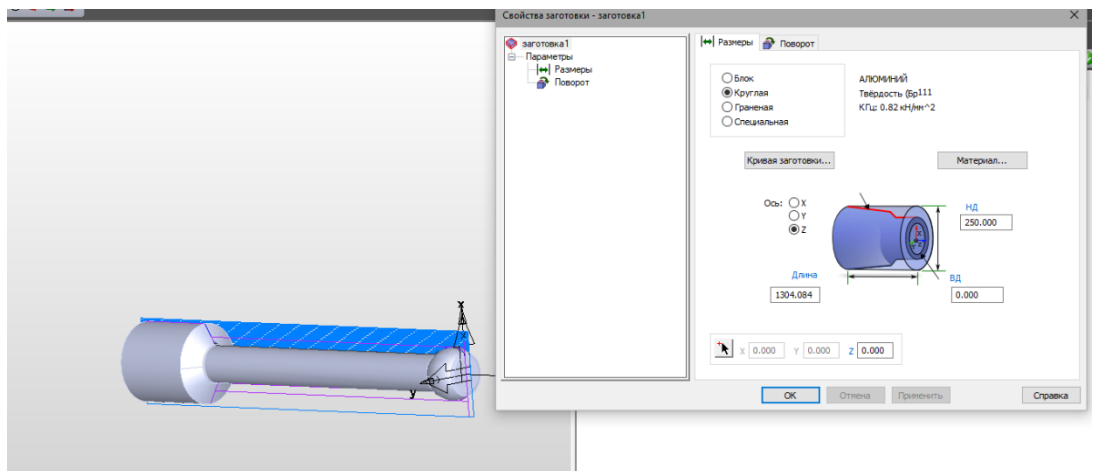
Загальний вигляд імпортування деталі та обраних параметрів заготовки
